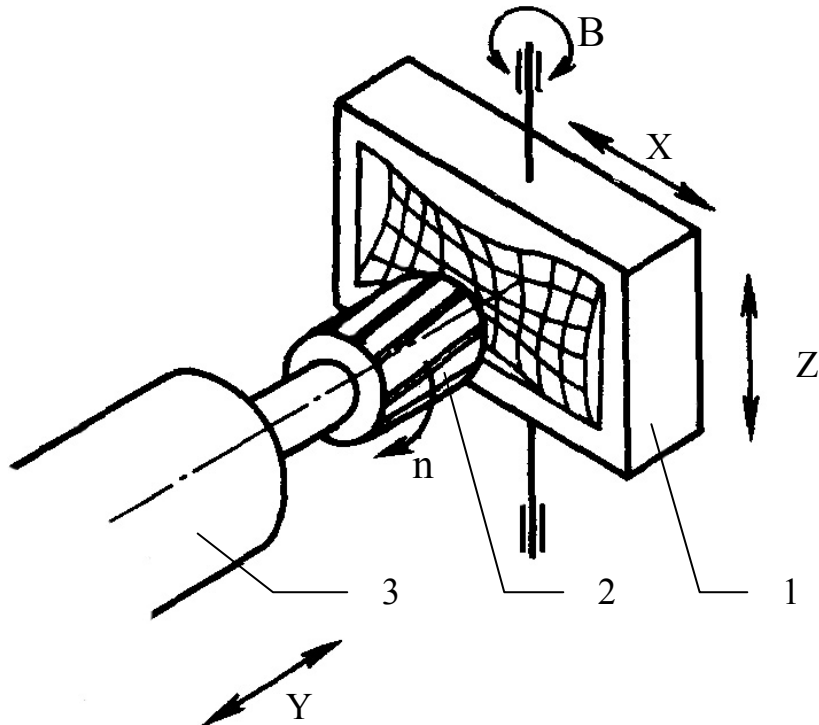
Схема копировально-фрезерного станка, обеспечивающая четыре перемещения
